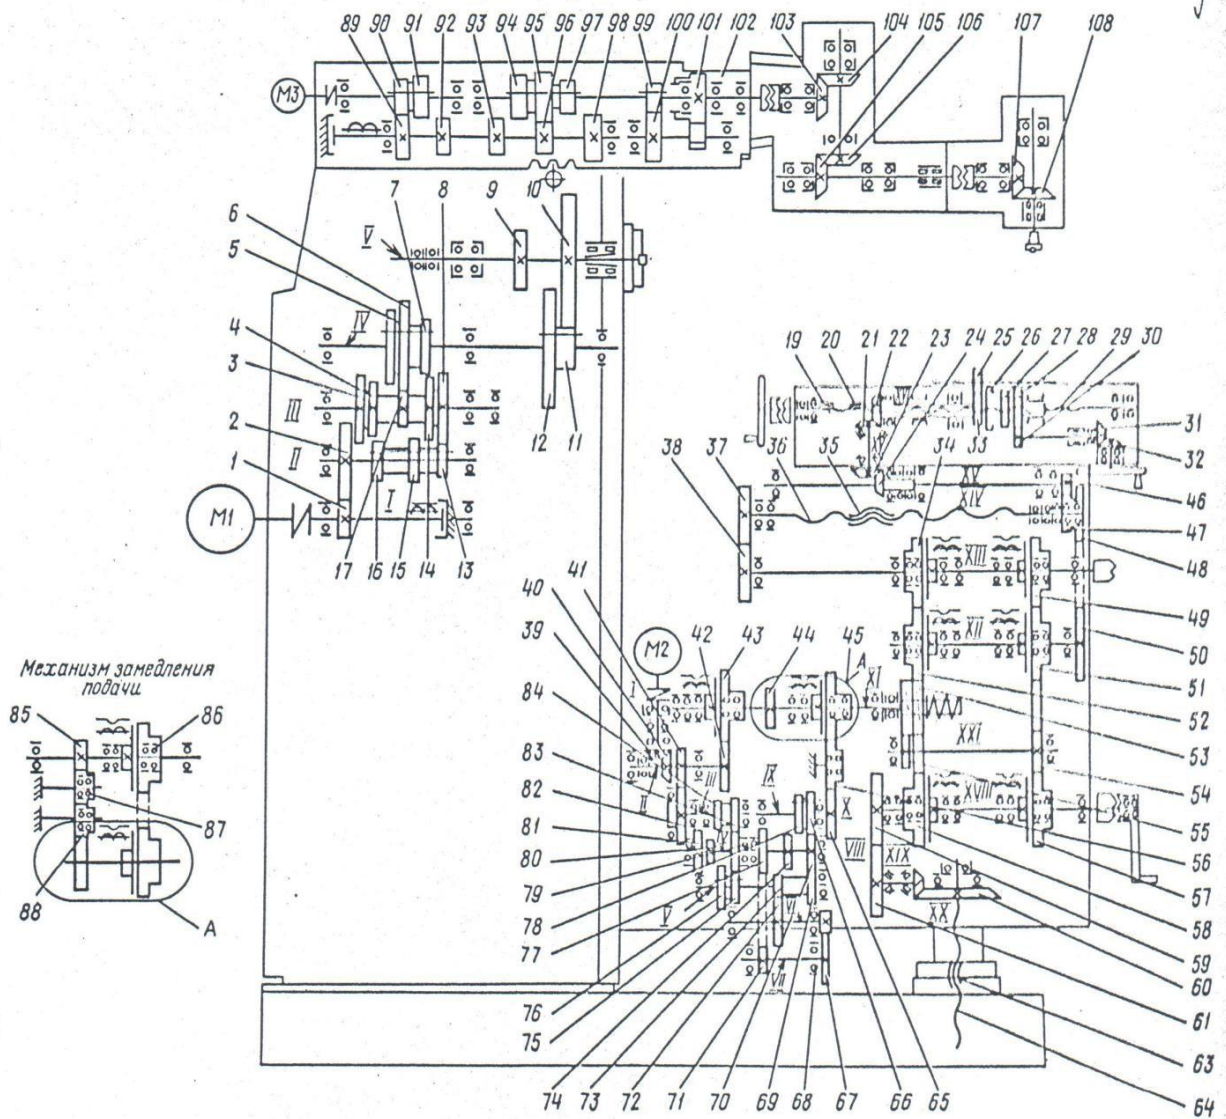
Схема кинематическая консольно — фрезерных станков моделей 6Р82Ш и 6Р83Ш
